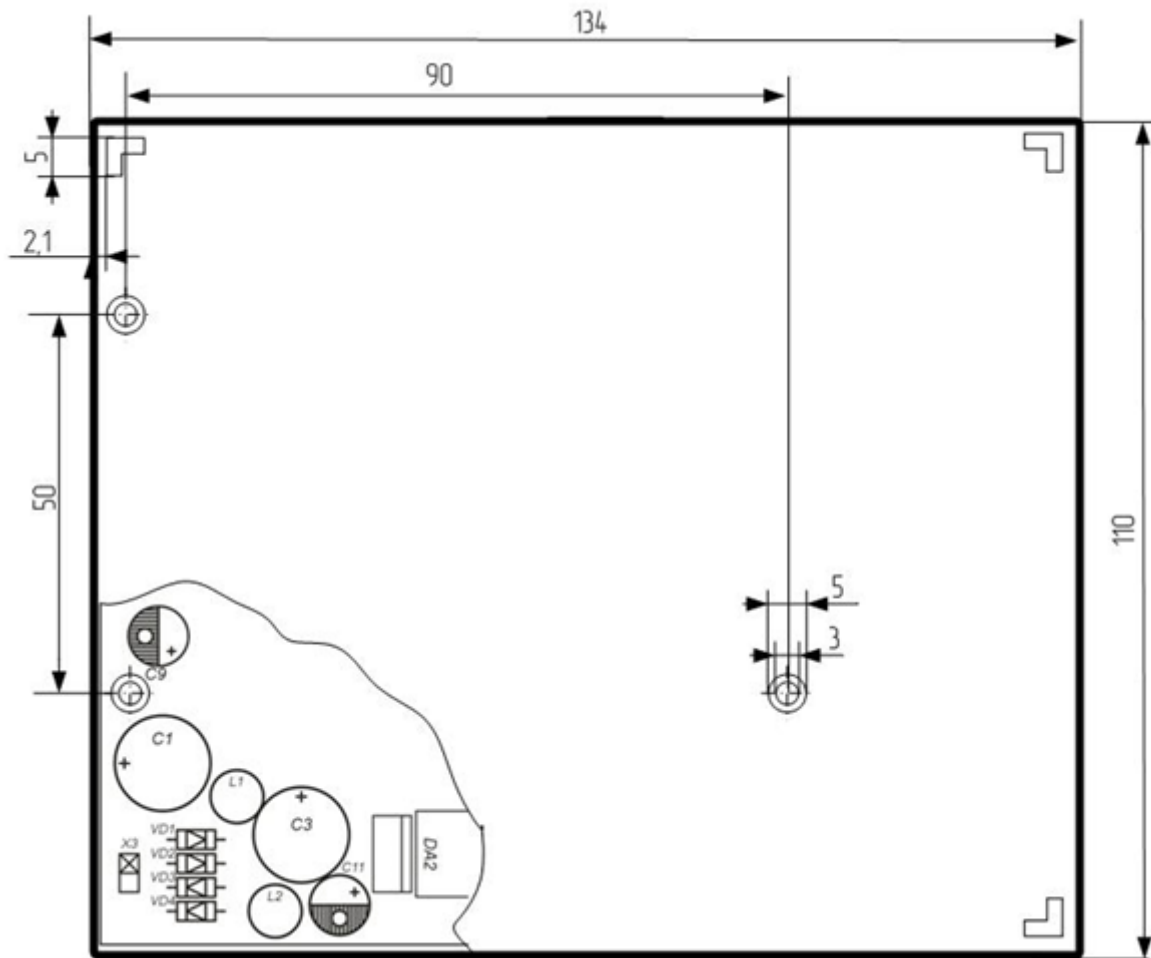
Ескізне креслення корпусу електронних ваг (вигляд ззаду)
